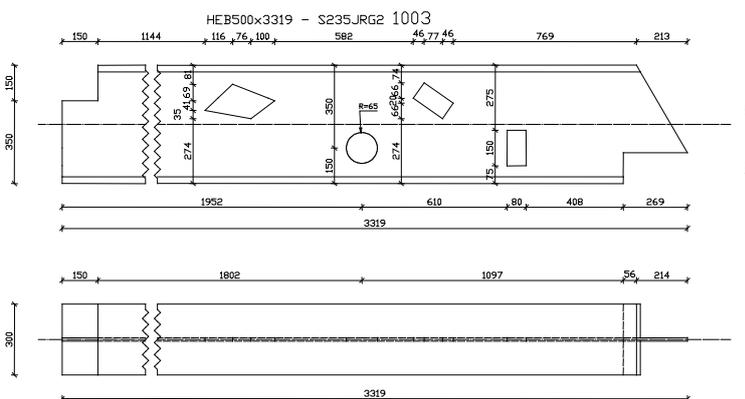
Pièce secondaire – Style de traçage : Poutre Devant, Dessus
